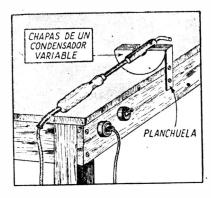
Forma de hacer un buen posa-soldador.
